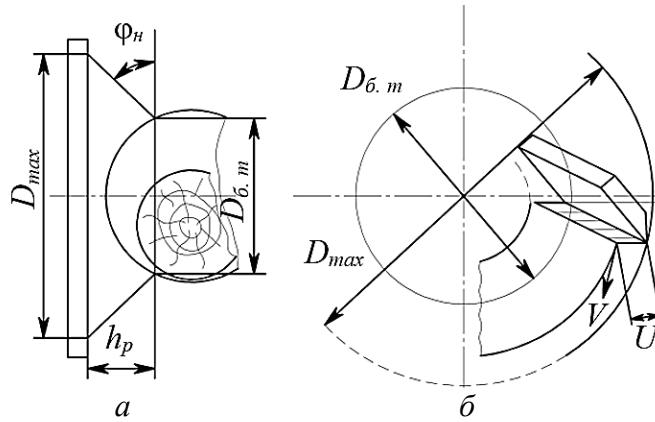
Параметры фрезерования малоножевыми торцово-коническими фрезами:
